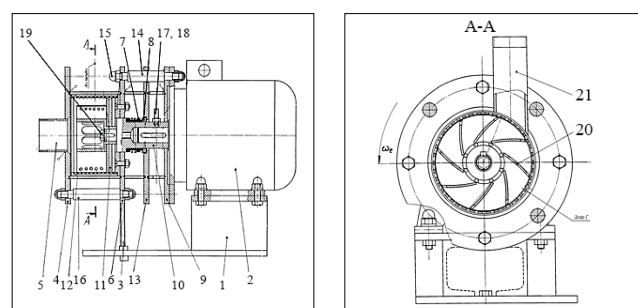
Общая схема дисмембратора: 1 – площадка крепления; 2 – двигатель; 3 – опорная шпилька; 4 – корпус; 5 – всасывающий патрубок; 6, 9 – проставки; 7 – муфта торцевая; 8 – торцевое уплотнение, кольцо керамическое; 10 – вал-втулка; 11 – крыльчатка; 12 – статор; 13 – фланец; 14 – шпилька; 15 – колпачковая гайка; 16 – шпилька; 17 – винт; 18 – контргайка; 19 – болт; 20 – лопасть крыльчатки; 21 – выходной патрубок
